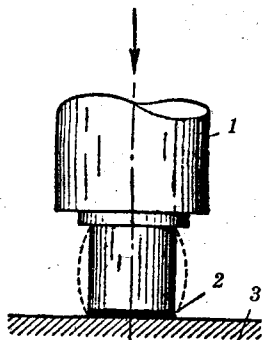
Осадка посадочного участка под обойму шарикового или роликового подшипника:
